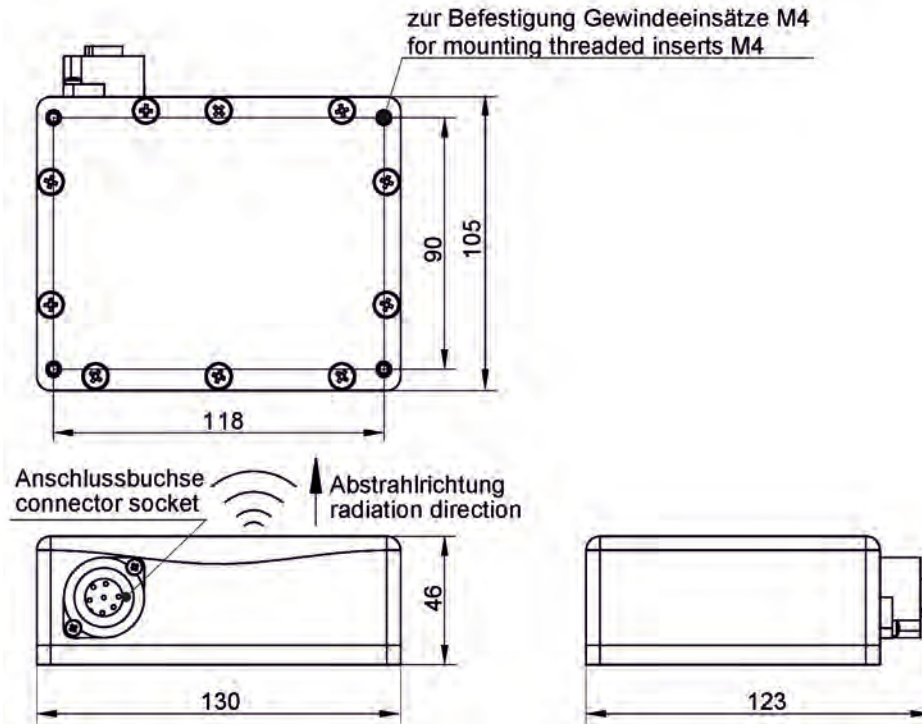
Dimensions du capteur radar OFR types H00/EVG dans le boîtier du capteur
